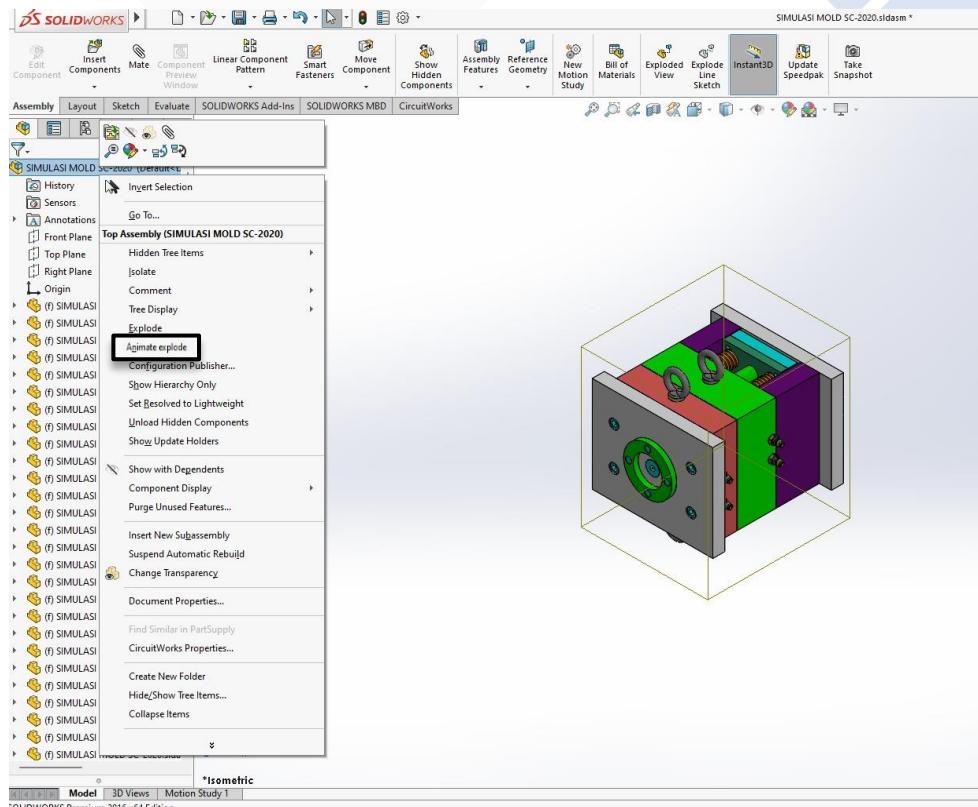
Proses Assembly Desain Cetakan Produk Holder
